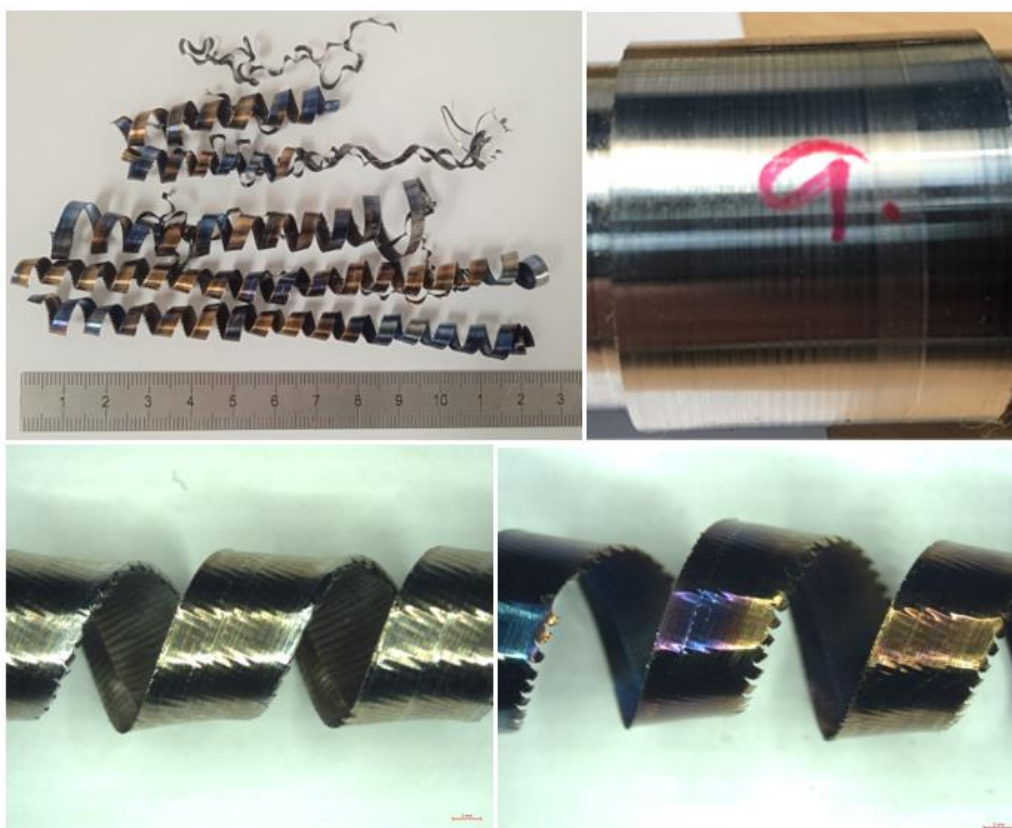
Třísky a obroběný povrch, VBD 6.
